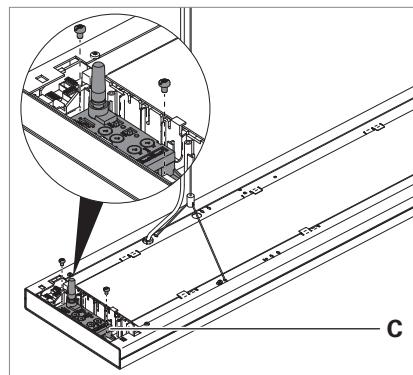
Modulo radio in un apparecchio d'illuminazione a sospensione LAVIGO.
